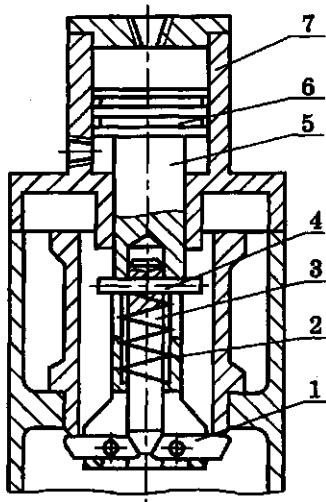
Приспособление для снятия гильзы цилиндра: 1 — захват; 2 — пружина; 3 — клин; 4 — штифт; 5 — шток; 6 — поршень; 7 — гидроцилиндр
